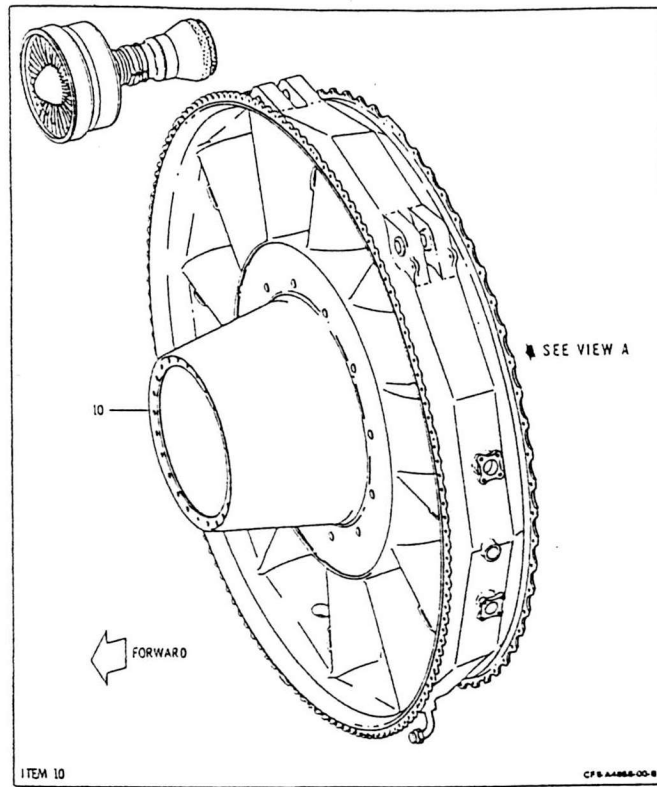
แสดงภาพ F Module (Low Pressure Turbine Assembly)
